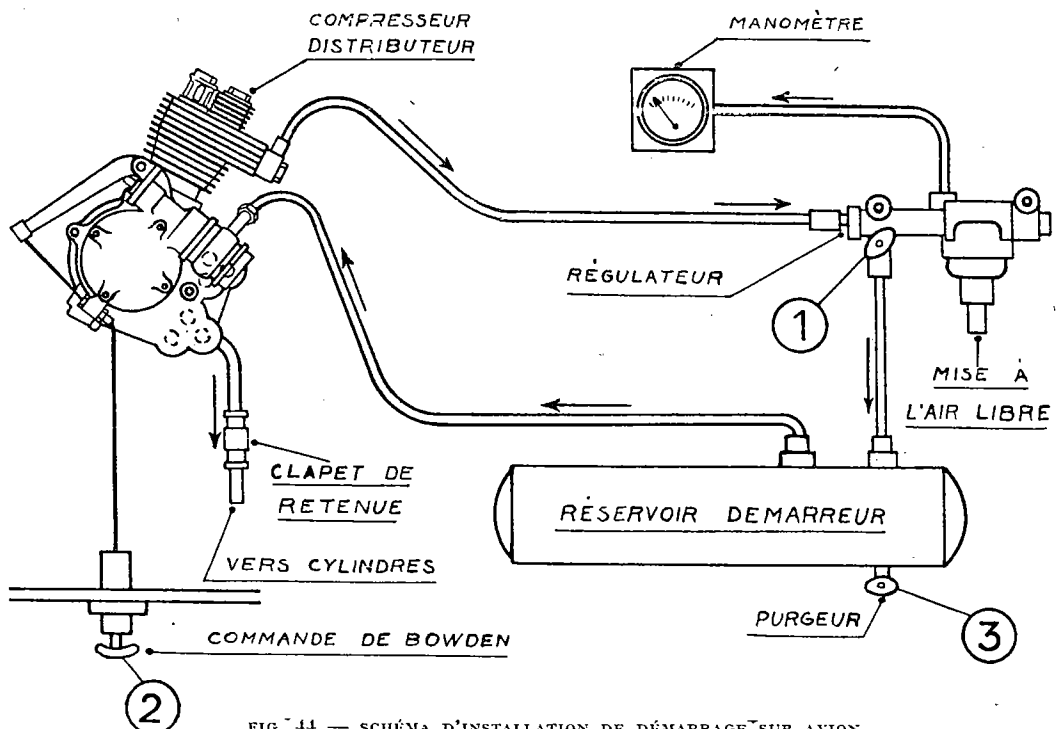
SCHÉMA D'INSTALLATION DE DÉMARRAGE SUR AVION
